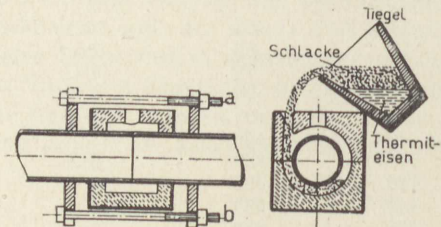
Um die Rohrenden gelegte Form für Thermitschweißen und Gießvorgang.
